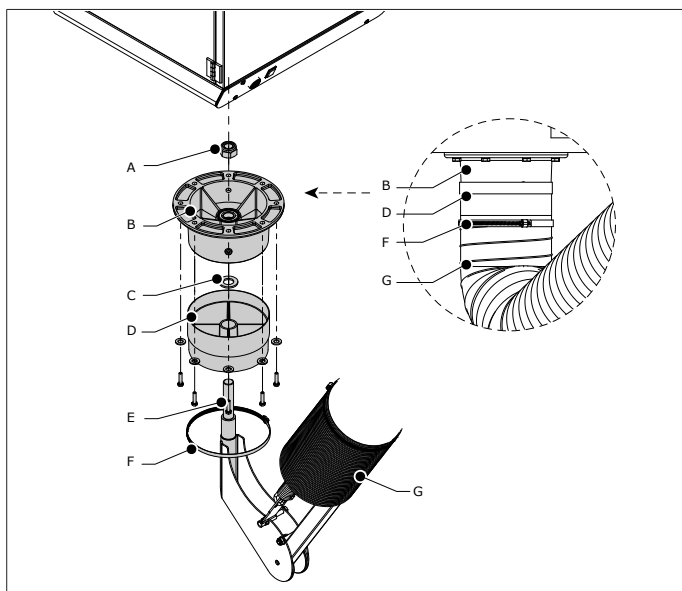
Установка вытяжного устройства на стационарный фильтр
